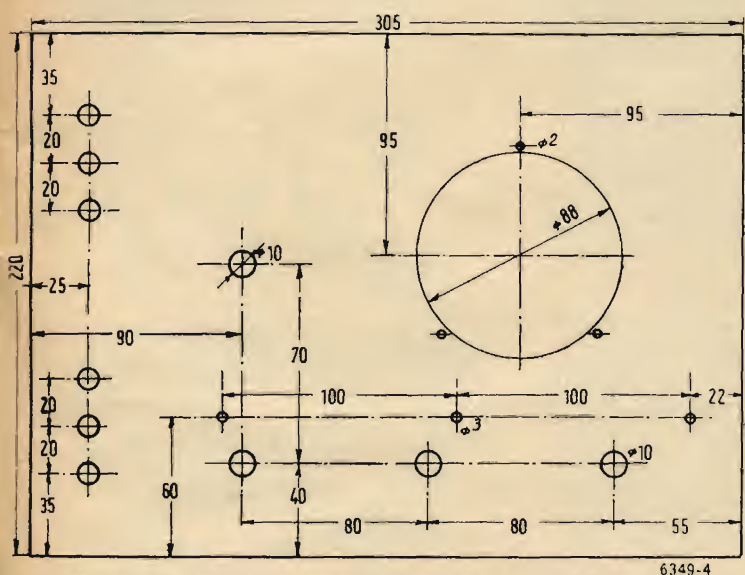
Dimensioni del pannello frontale e piano di foratura del medesimo.
